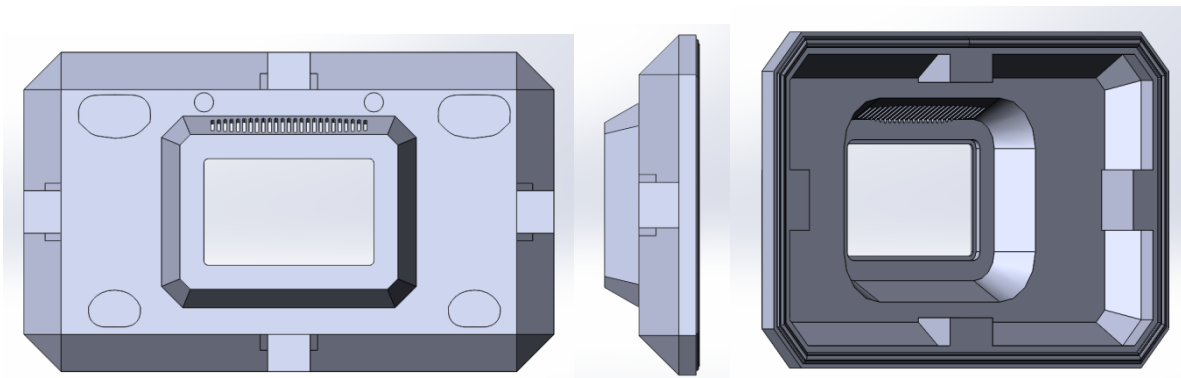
Модель крышки для рабочей камеры 3д-принтера
